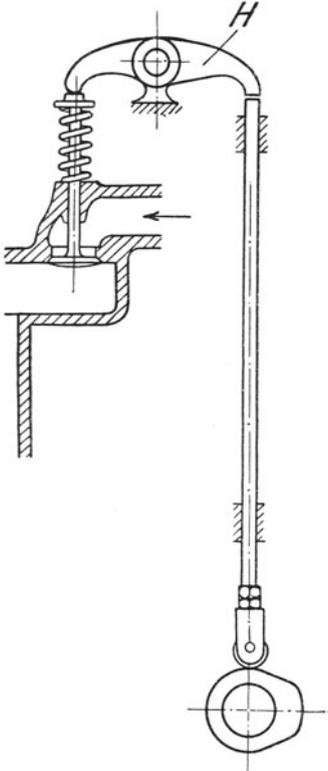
Oben gesteuertes „hängendes“ Ventil mit untenliegender Nockenwelle
